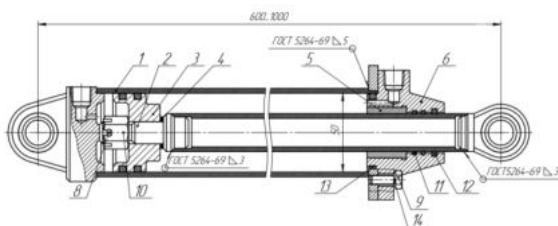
Исходный чертеж силового гидроцилиндра двустороннего действия
